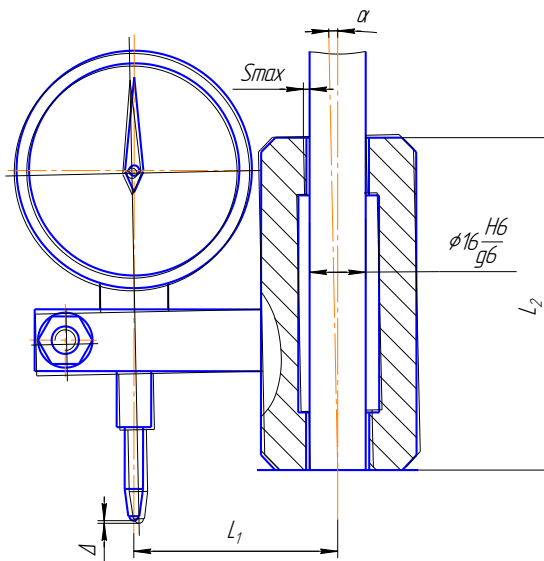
Схема формування похибки вимірювання контрольного пристрою
